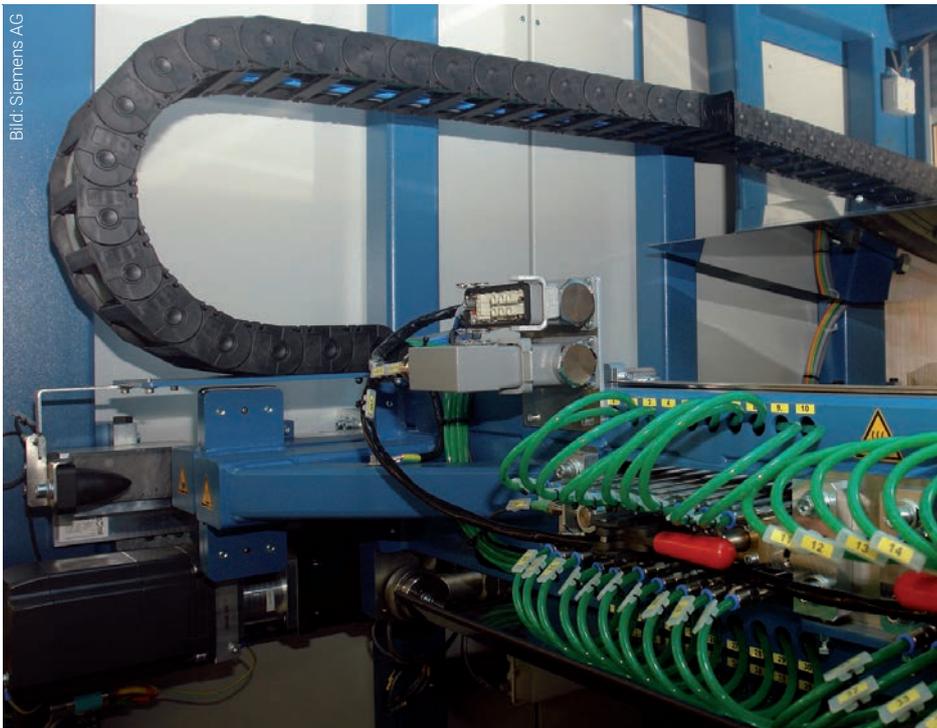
| Die Firma Atlantique Automatisierungstechnik rüstet Heiß-Gas-Schweißanlagen zum thermischen Verbinden von Hightech-Kunststoffteilen elektrotechnisch aus und hat dort nun erstmals die Motorstarter Simatic ET 200SP verbaut.
